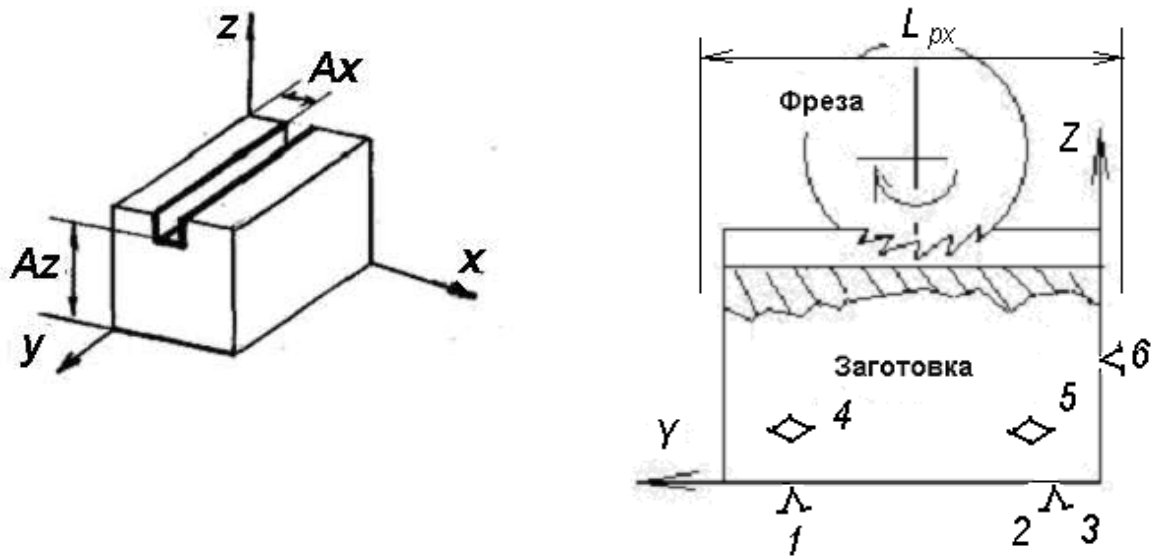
Схема установки та схема обробки відкритого пазу.
